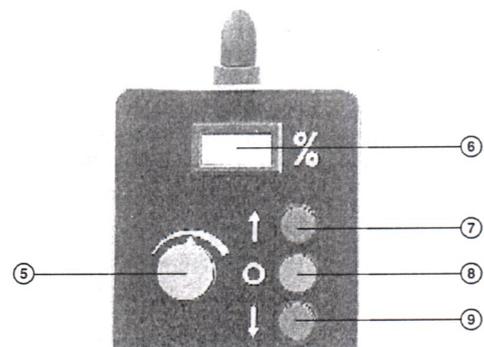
Vista da face frontal da unidade de controle ID Weld 2500
